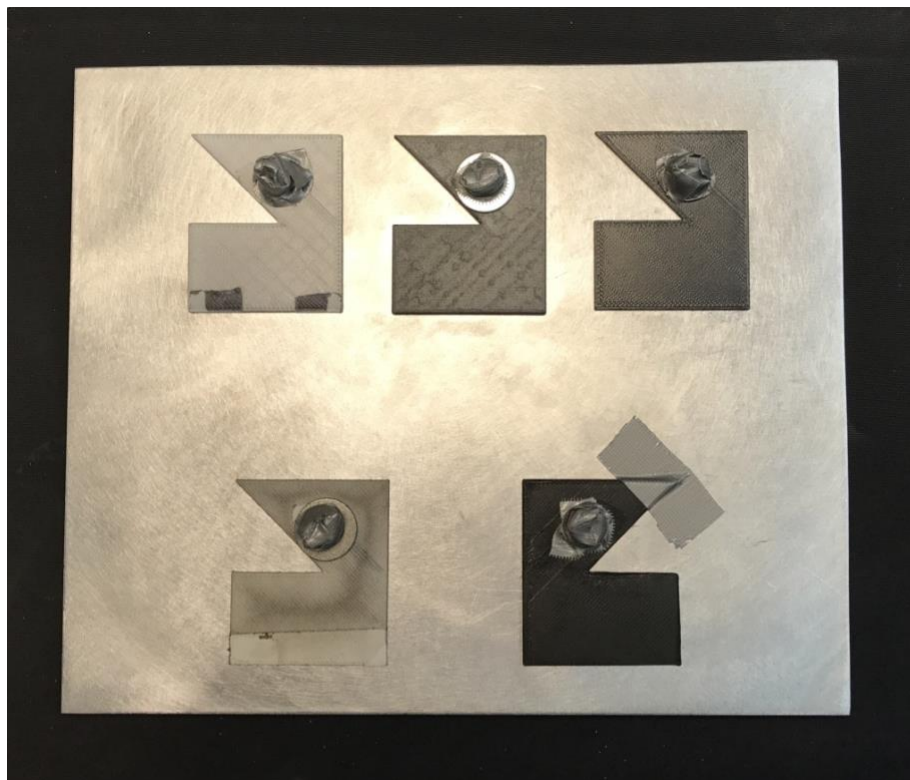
Aspecto de la placa-probeta después del segundo ensayo.
